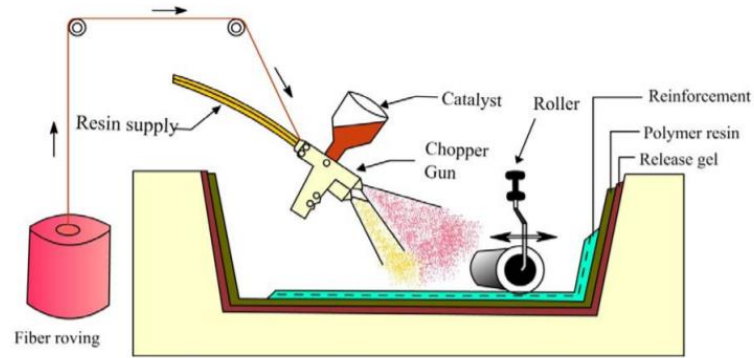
técnica de moldeo por proyección simultánea, imagen de *Hand Lay-up and Spray Lay-up* lectura 5.4
